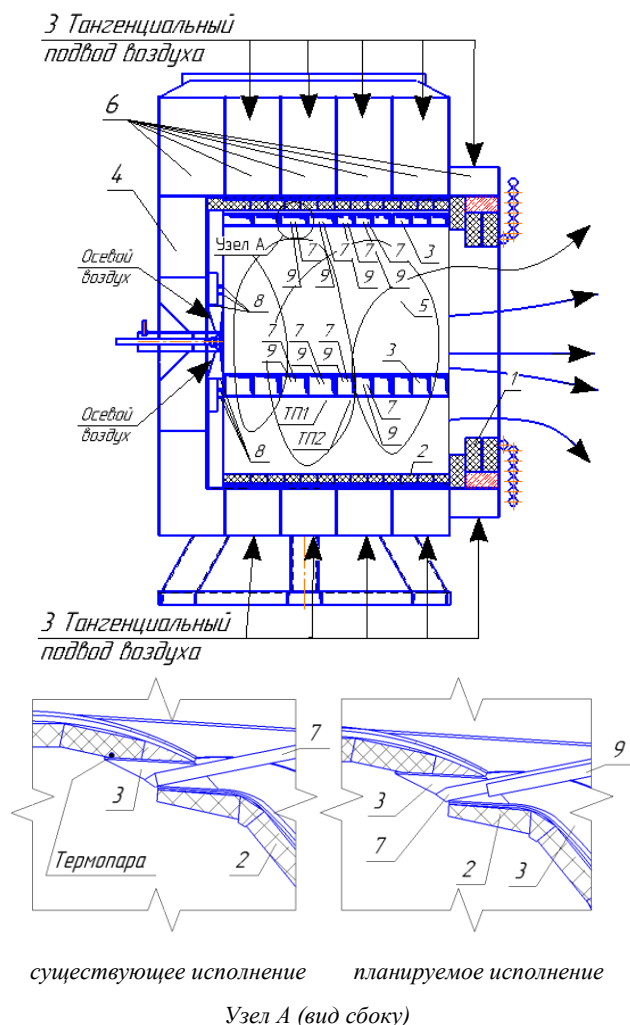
Конструкция газо-мазутного ЦВП мощностью 65 МВт: 1 – пережим; 2 – обмуровка; 3 – тангенциальный подвод воздуха; 4 – торцевая вихревая камера; 5 – камера сгорания; 6 – воздушные обечайки; 7 – тангенциальные газовые сопла; 8 – аксиальные, торцевые газовые сопла; 9 – второй ряд тангенциальных газовых сопел.
